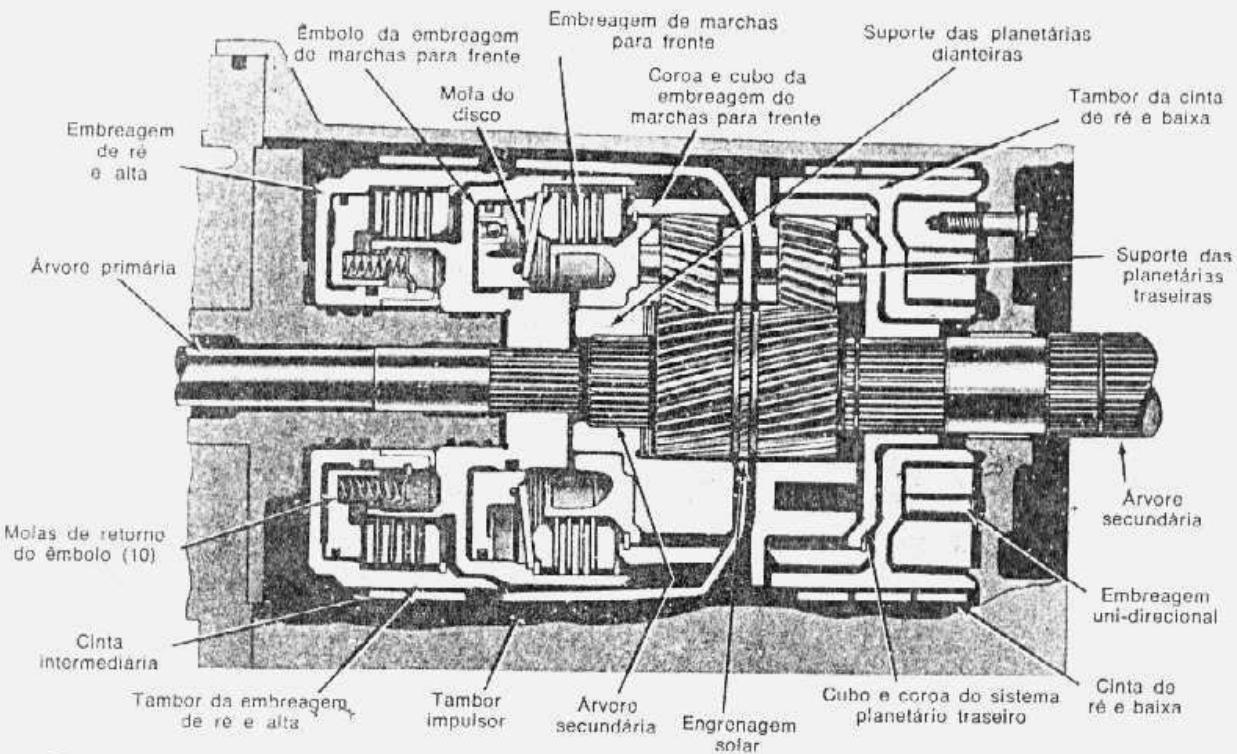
conjunto de engrenagens, embreagens e cintas da transmissão
